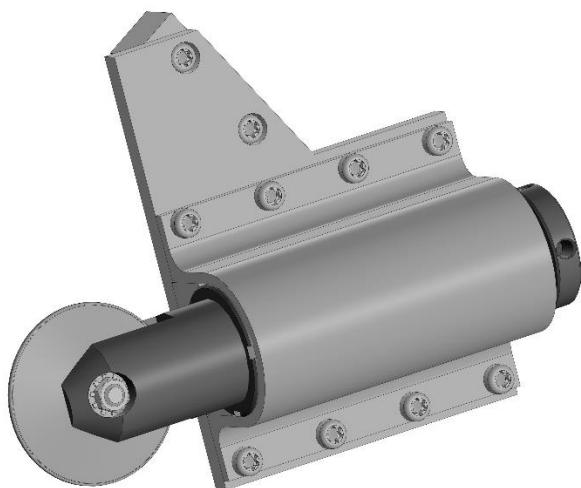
Модель нового обкатывающего устройства для токарного станка с ЧПУ 16К20Ф3
